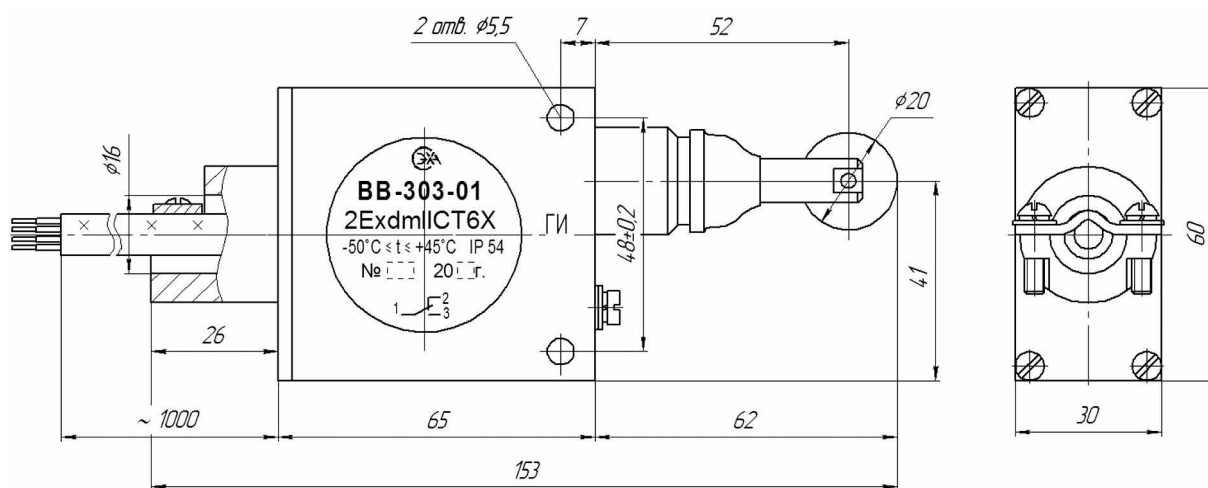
б. Габаритные и установочные размеры ВВ-303-01
